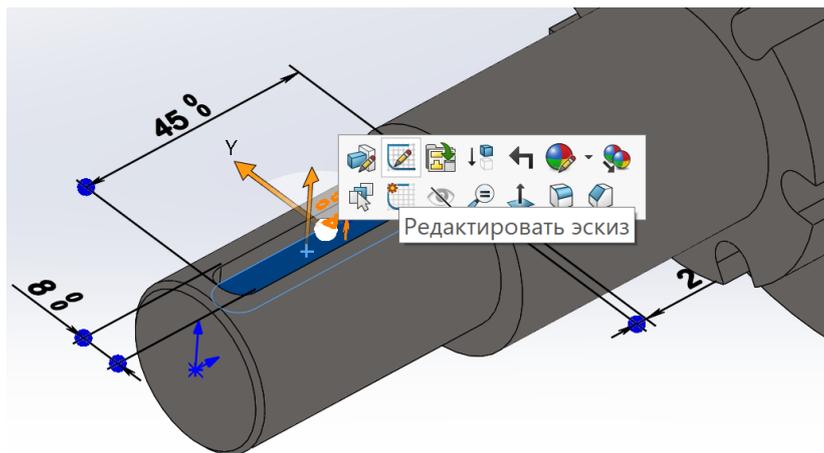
Редагування ескізу на поверхні деталі
